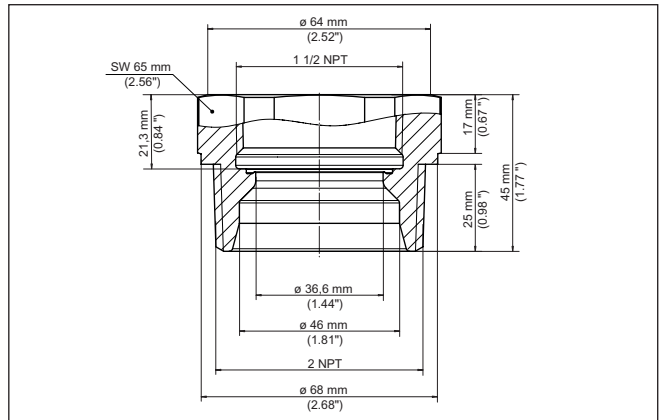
Maße Gewindeadapter 1½"NPT auf Gewinde 2"NPT
